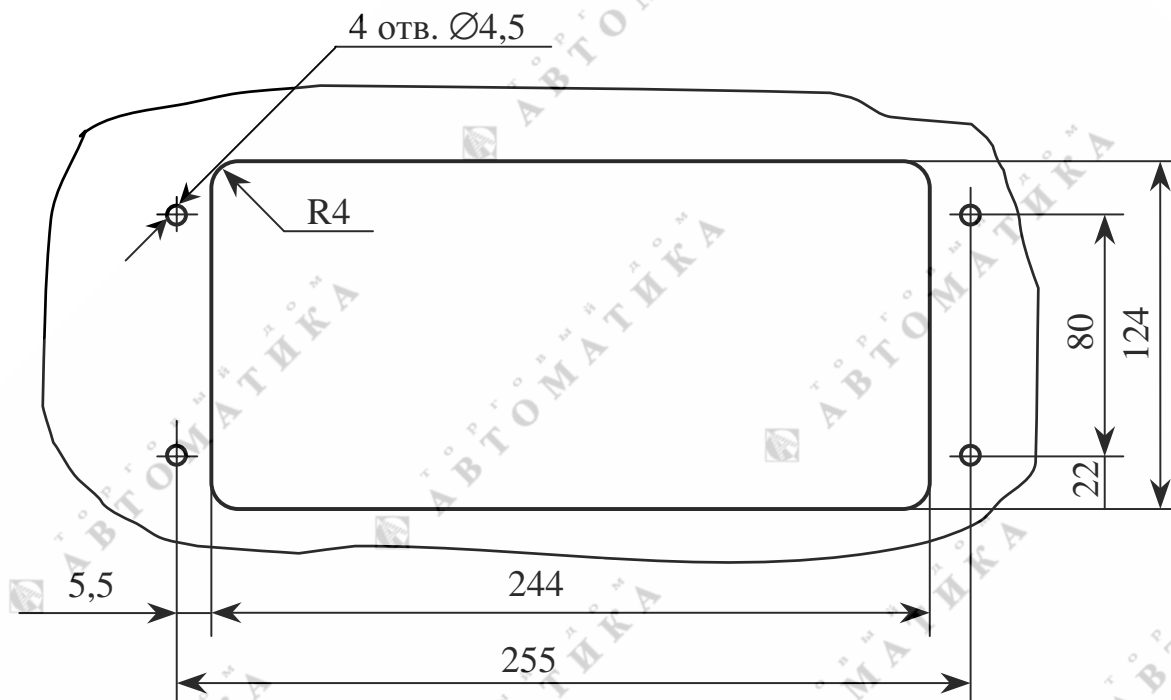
Разметка отверстий в щите для крепления блока преобразовательного
